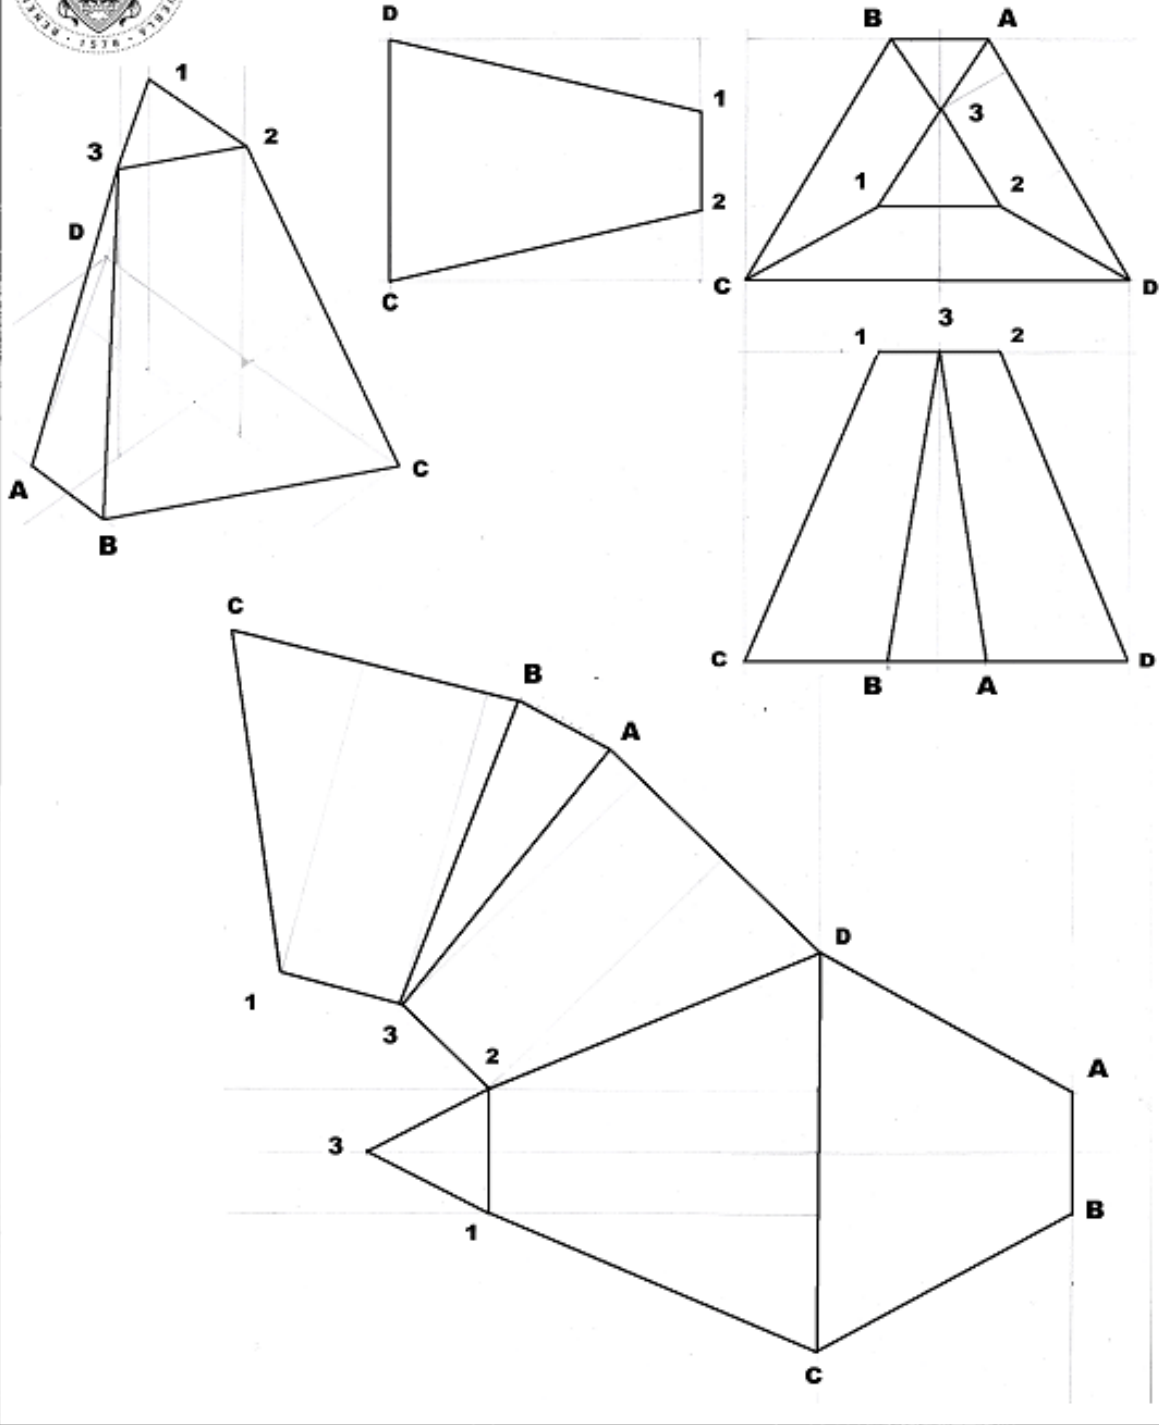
Práctica 45 Desarrollo y construcción de un trapezoido a triangulo
